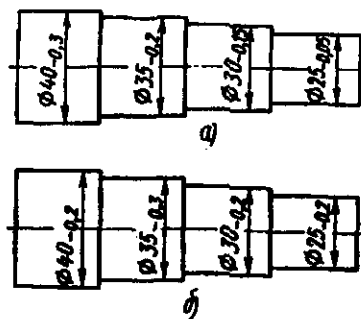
Эскизы для расчета копира: а – с неповторяющимися допусками; б – с повторяющимися допусками
